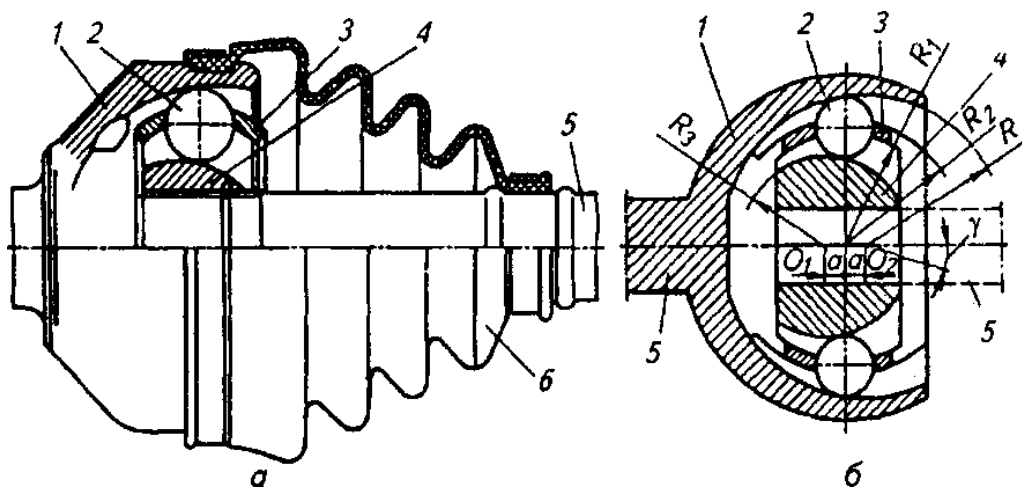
Шестишариковый карданный шарнир с делительными канавками типа «Бирфильд»: а — общий вид; б— в разрезе; 1 — корпус; 2— шарик; 3 — сепаратор; 4 — кулачок; 5 — вал; 6 — защитный чехол
